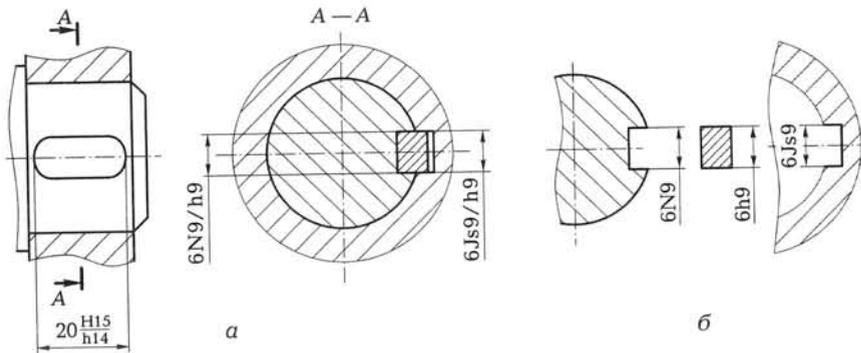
Обозначение полей допусков деталей соединения и посадок шпоночного сопряжения:
